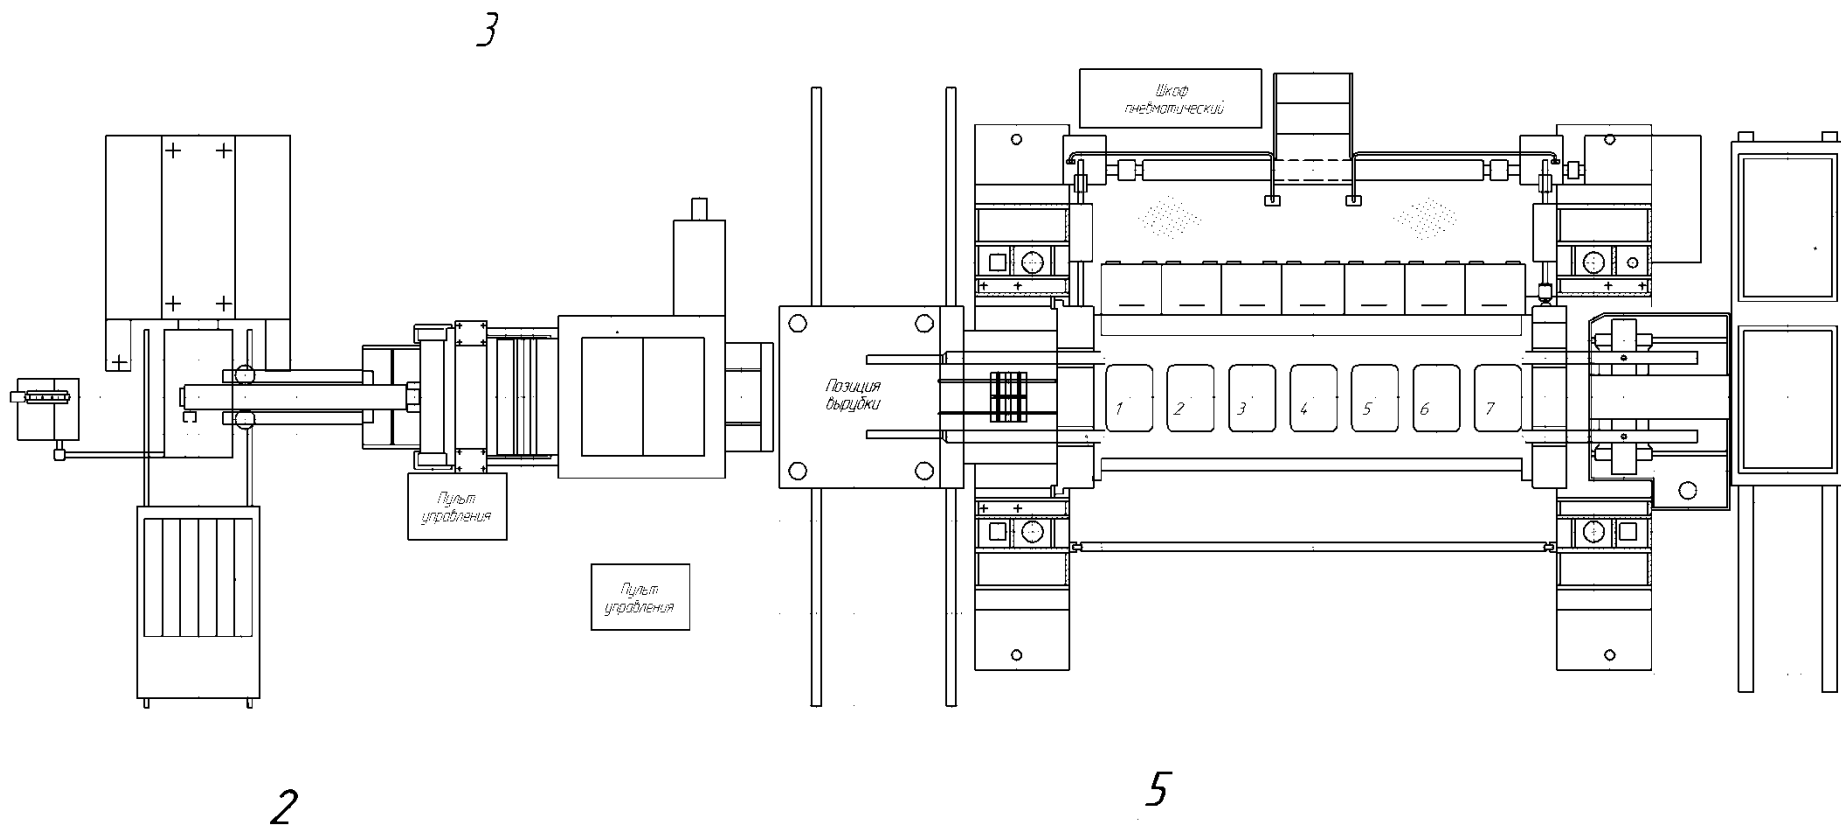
Вид сверху на рабочую зону прессы
